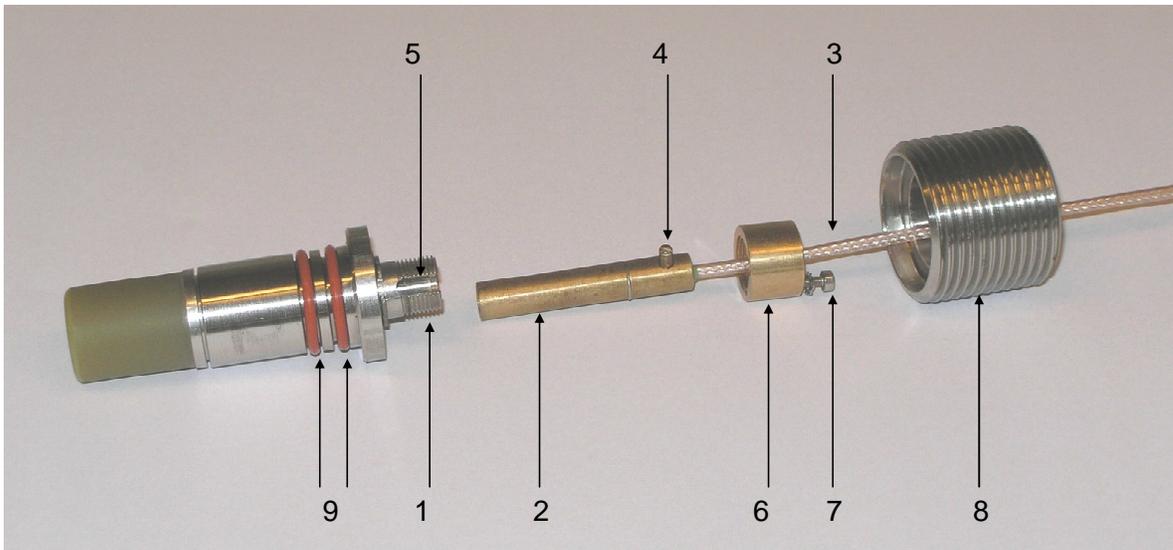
Baugruppe Messwertaufnehmer und Anschluss
